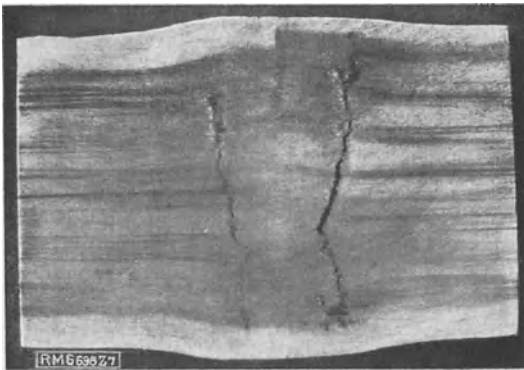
Risse in einer gehämmerten Stumpfschweißung (V = 1,4).
